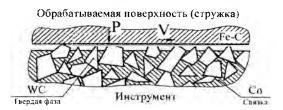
Схема контакта обрабатываемой поверхности и рабочей поверхности гвердоспливного инструмента
